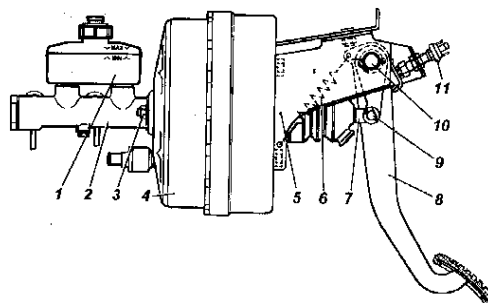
Привод главного цилиндра: 1 -бачок; 2 -картер главного тормозного цилиндра; 3 -гайка; 4 -вакуумный усилитель; 5 -кронштейн педали тормоза; 6 -оттяжная пружина; 7 -вилка; 8 -педаль тормоза; 9 -палец; 10 -ось педали тормоза; 11 -выключатель сигнала торможения
